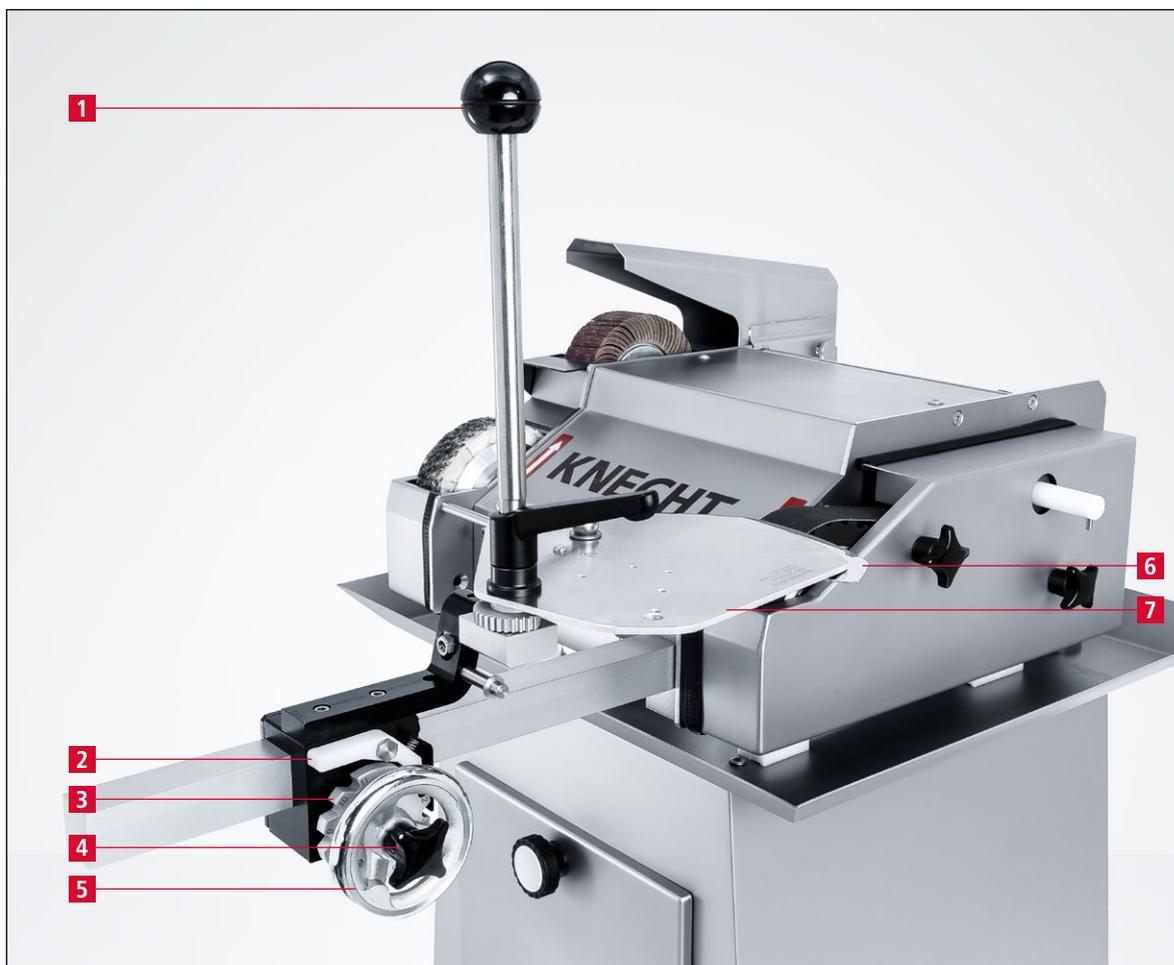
Общий вид устройства для ленточной заточки HV 161
